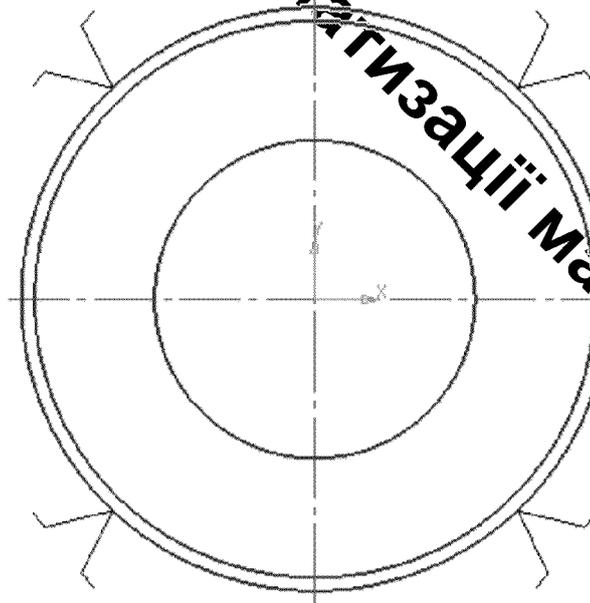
Схема закріплення заготовки в захваті промислового робота
